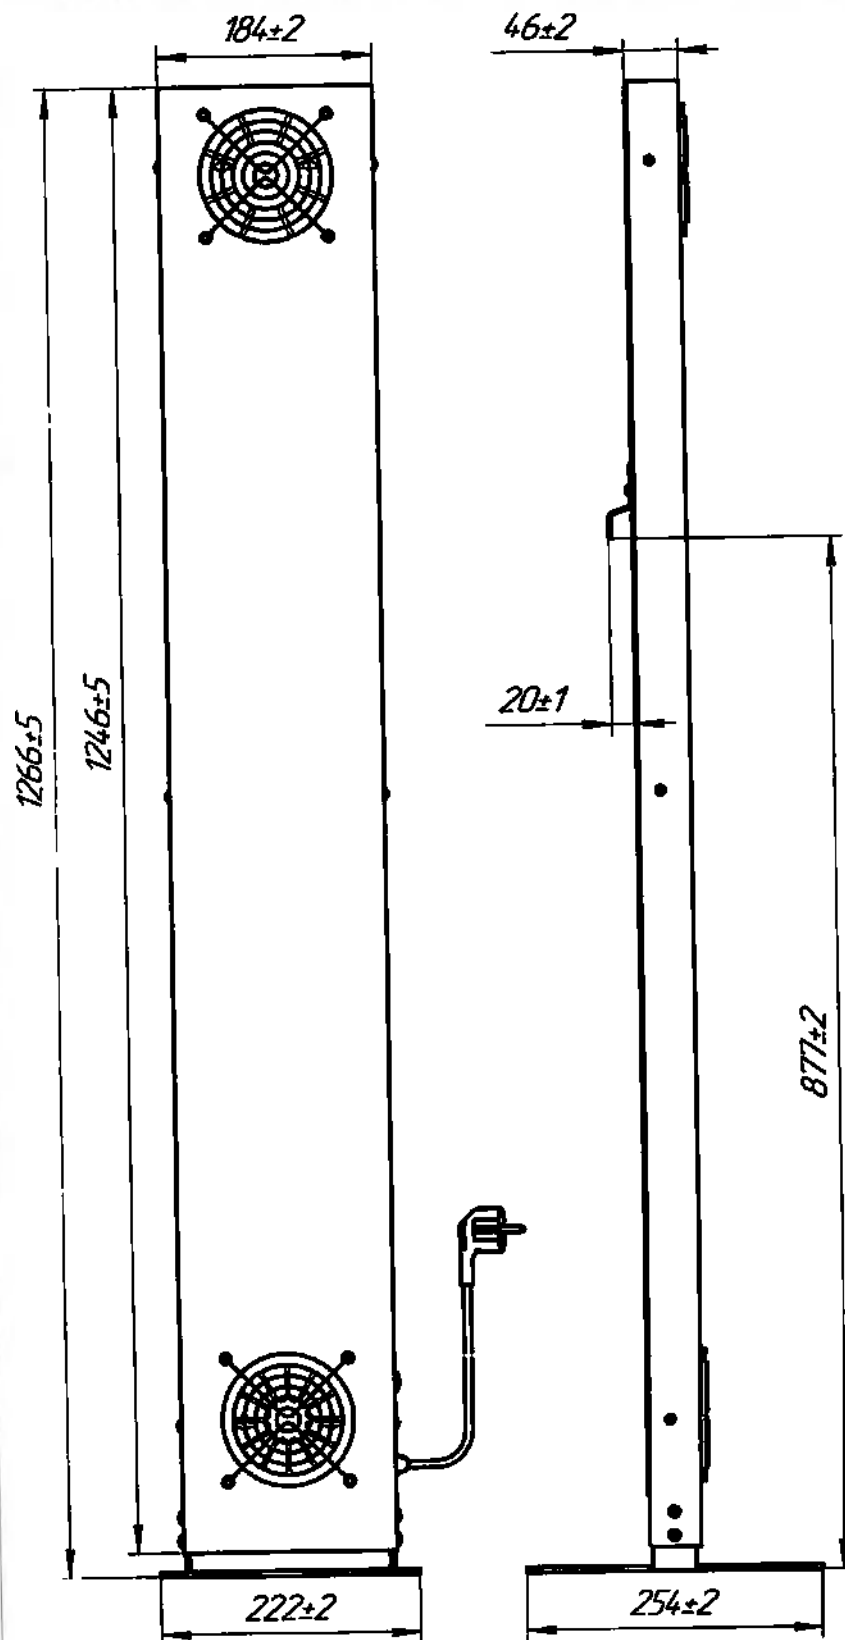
Облучатель РВ-30, РВ-40 и РВ-80 смонтированный на опорную стойку
